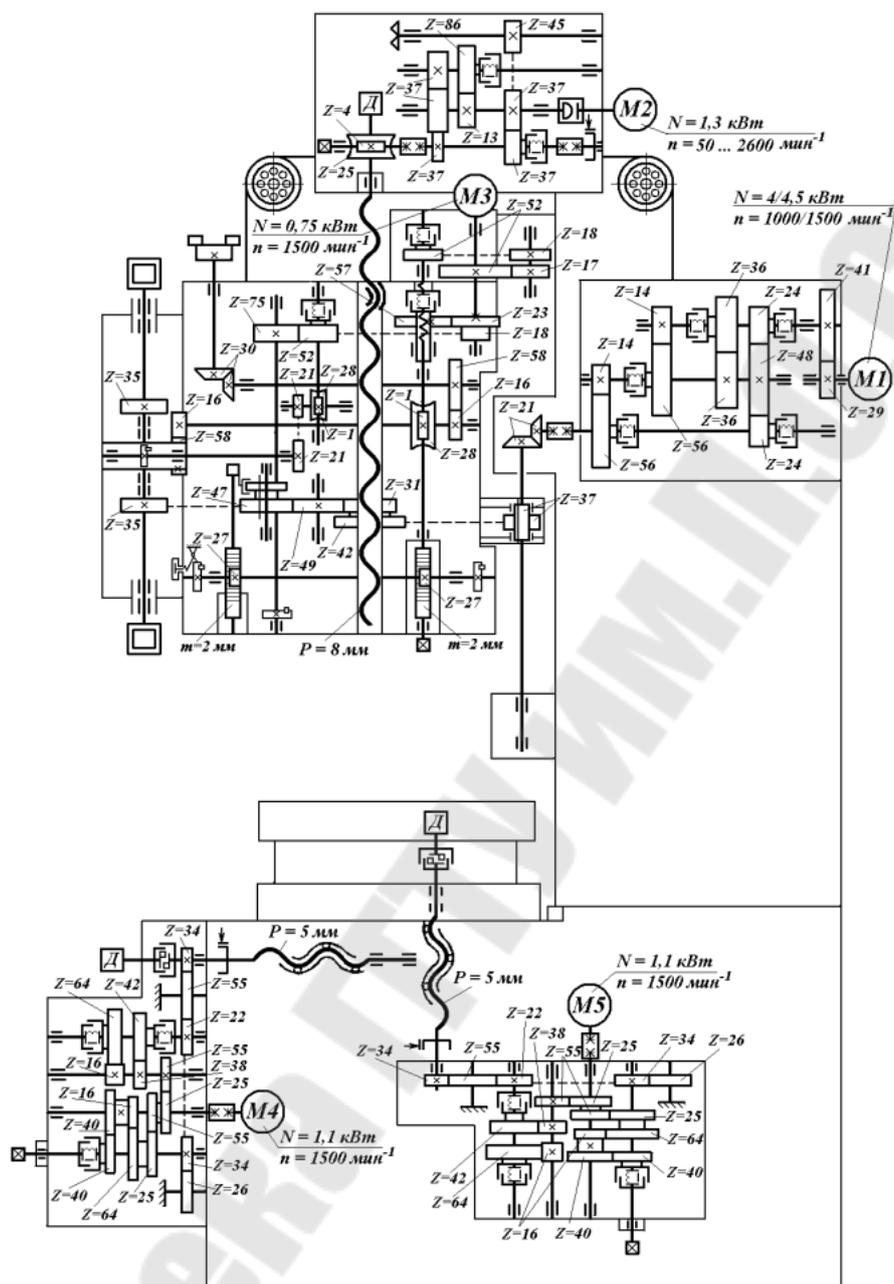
Кинематическая схема вертикально-сверлильного станка 2P135Φ2-1
